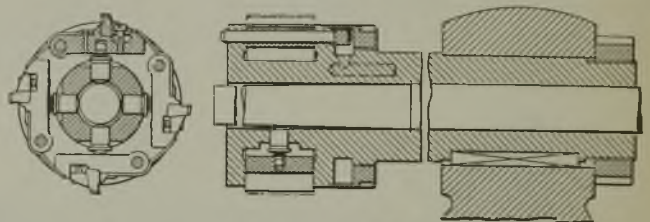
Schleppmesser-Gewindeschneidkopf für kegelliges Gewinde.
